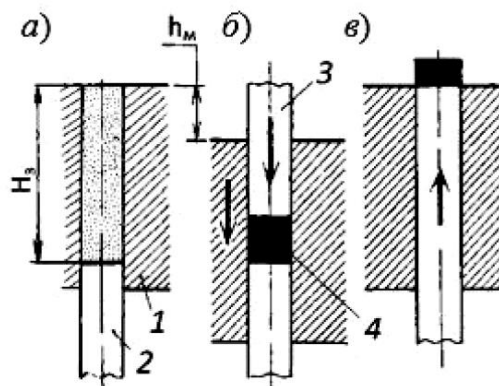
Схема пресс-формы с подвижной матрицей для двустороннего прессования: а – заполнение матрицы порошком; б – прессование; в – выталкивание заготовки: 1 – матрица; 2,3 – пуансоны; 4 – заготовка
